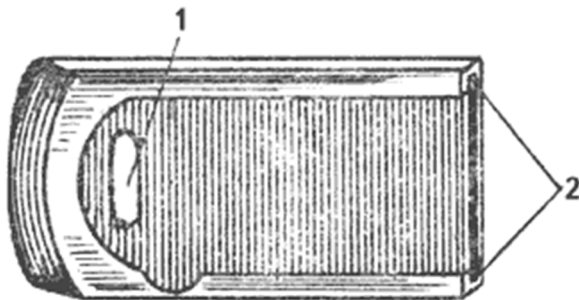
Крышка магазина: 1 – отверстие; 2 – пазы 36
